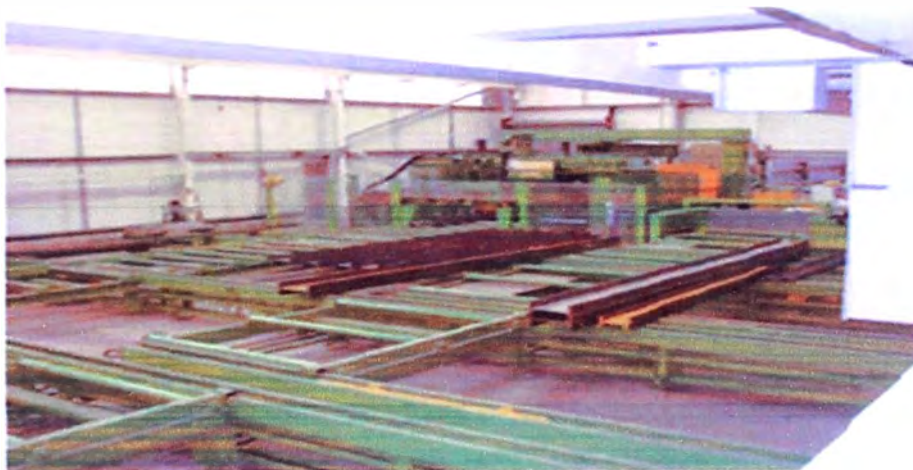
Sección CROSS TRANSFERS de la planta
